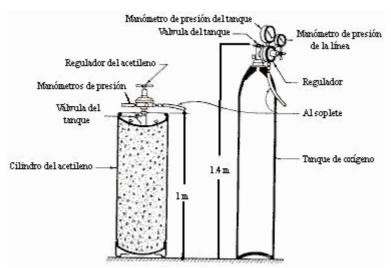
Tanque de oxígeno para una soldadura autógena Fuente: www.aprendizaje.com.
